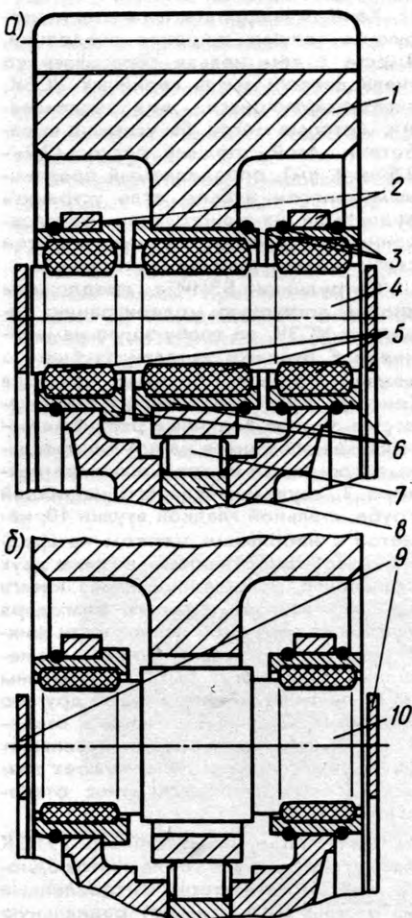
Упругая связь венца со ступицей с комбинированными упругими элементами: 1 — зубчатый венец; 2 — боковые фланцы; 3 — амортизатор; 4 — ролики; 5 — призонная втулка; 6 — болт; 7 — ступица; 8 — полиуретановый стакан; 9 — втулка амортизатора; 10 — стальная втулка
